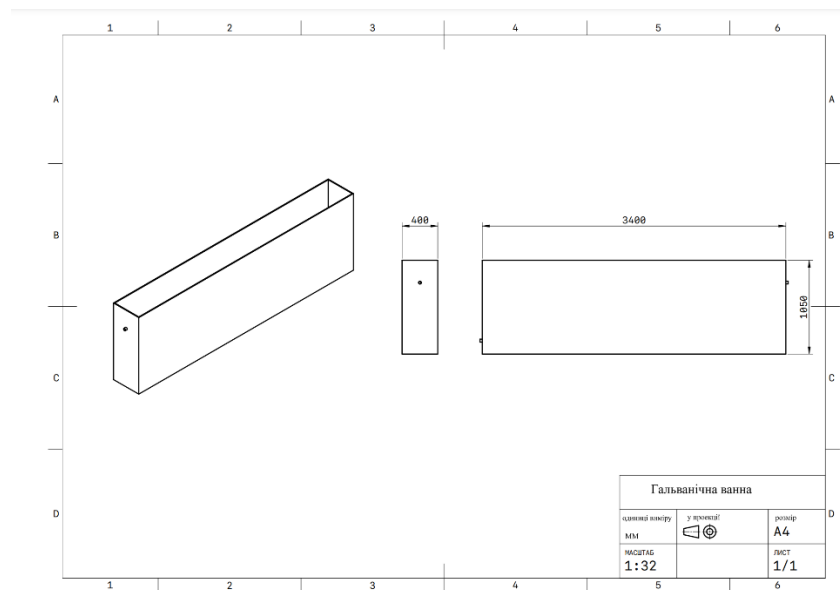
Креслення гальванічної ванни для анодування.
